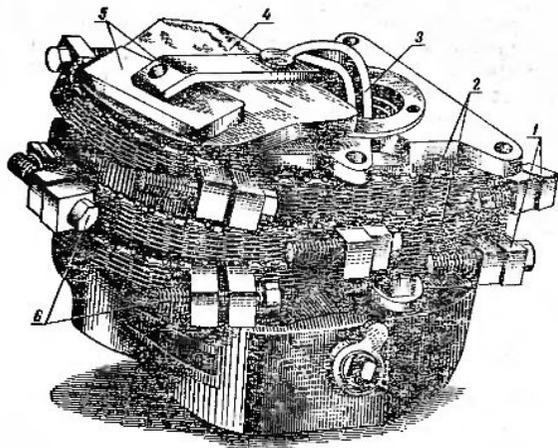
Заделка клевыми заплатами трещин и пробоя в корпусе коробки передач:
